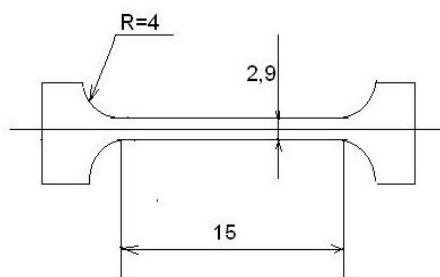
Геометрия и размеры рабочей части образца для испытаний на растяжение
